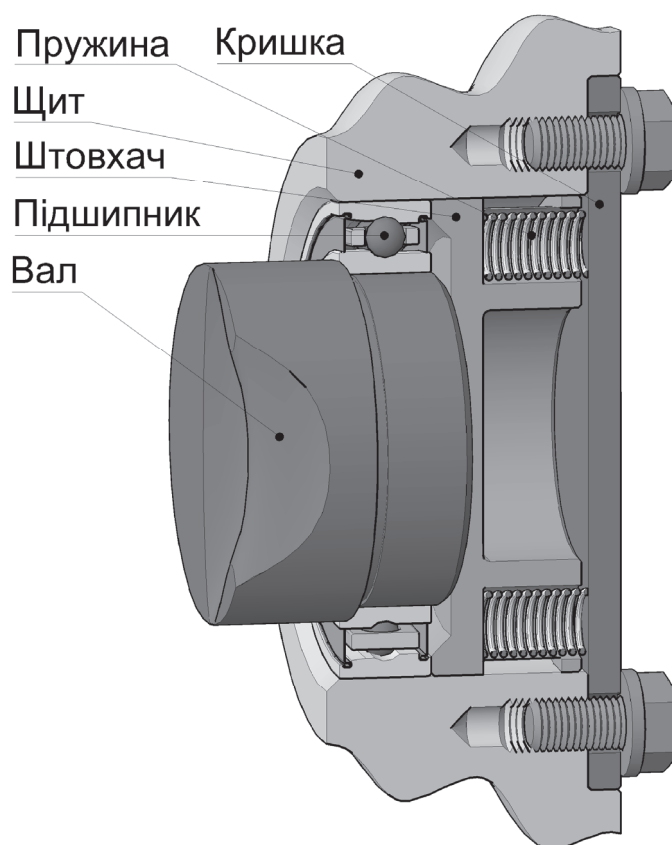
Конструкція підшипникового вузла для створення попереднього натягу
